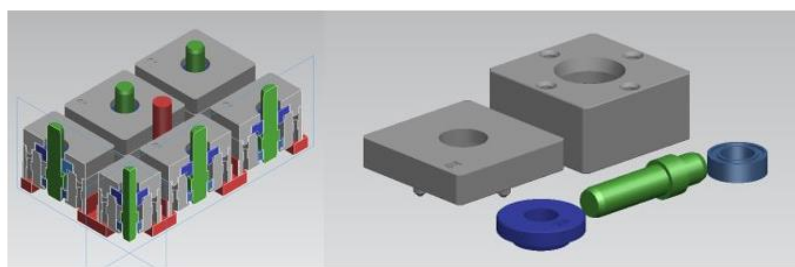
Piezas del conjunto (derecha) y corte del conjunto montado (izquierda).
